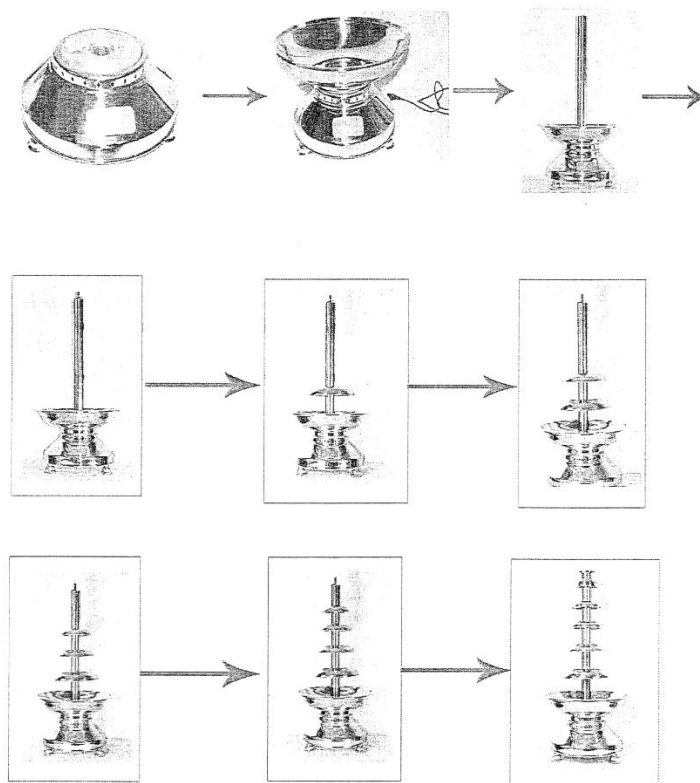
Сборка фонтана для шоколада ANT-8110
